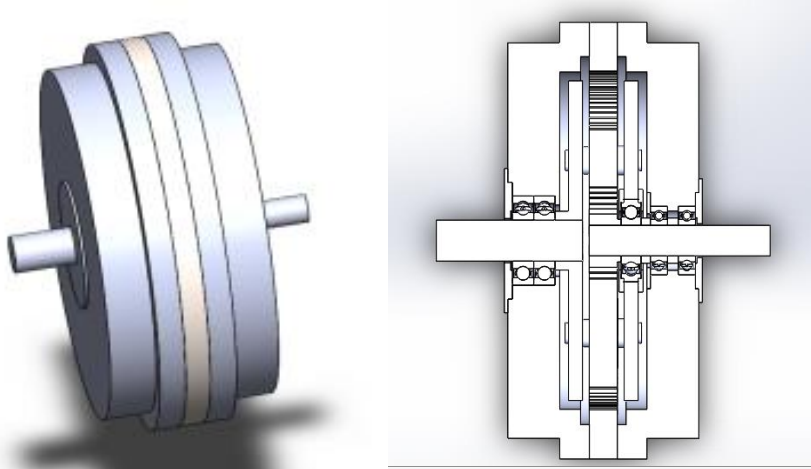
3D Poros & Sun Gear Single Stage Planetary
